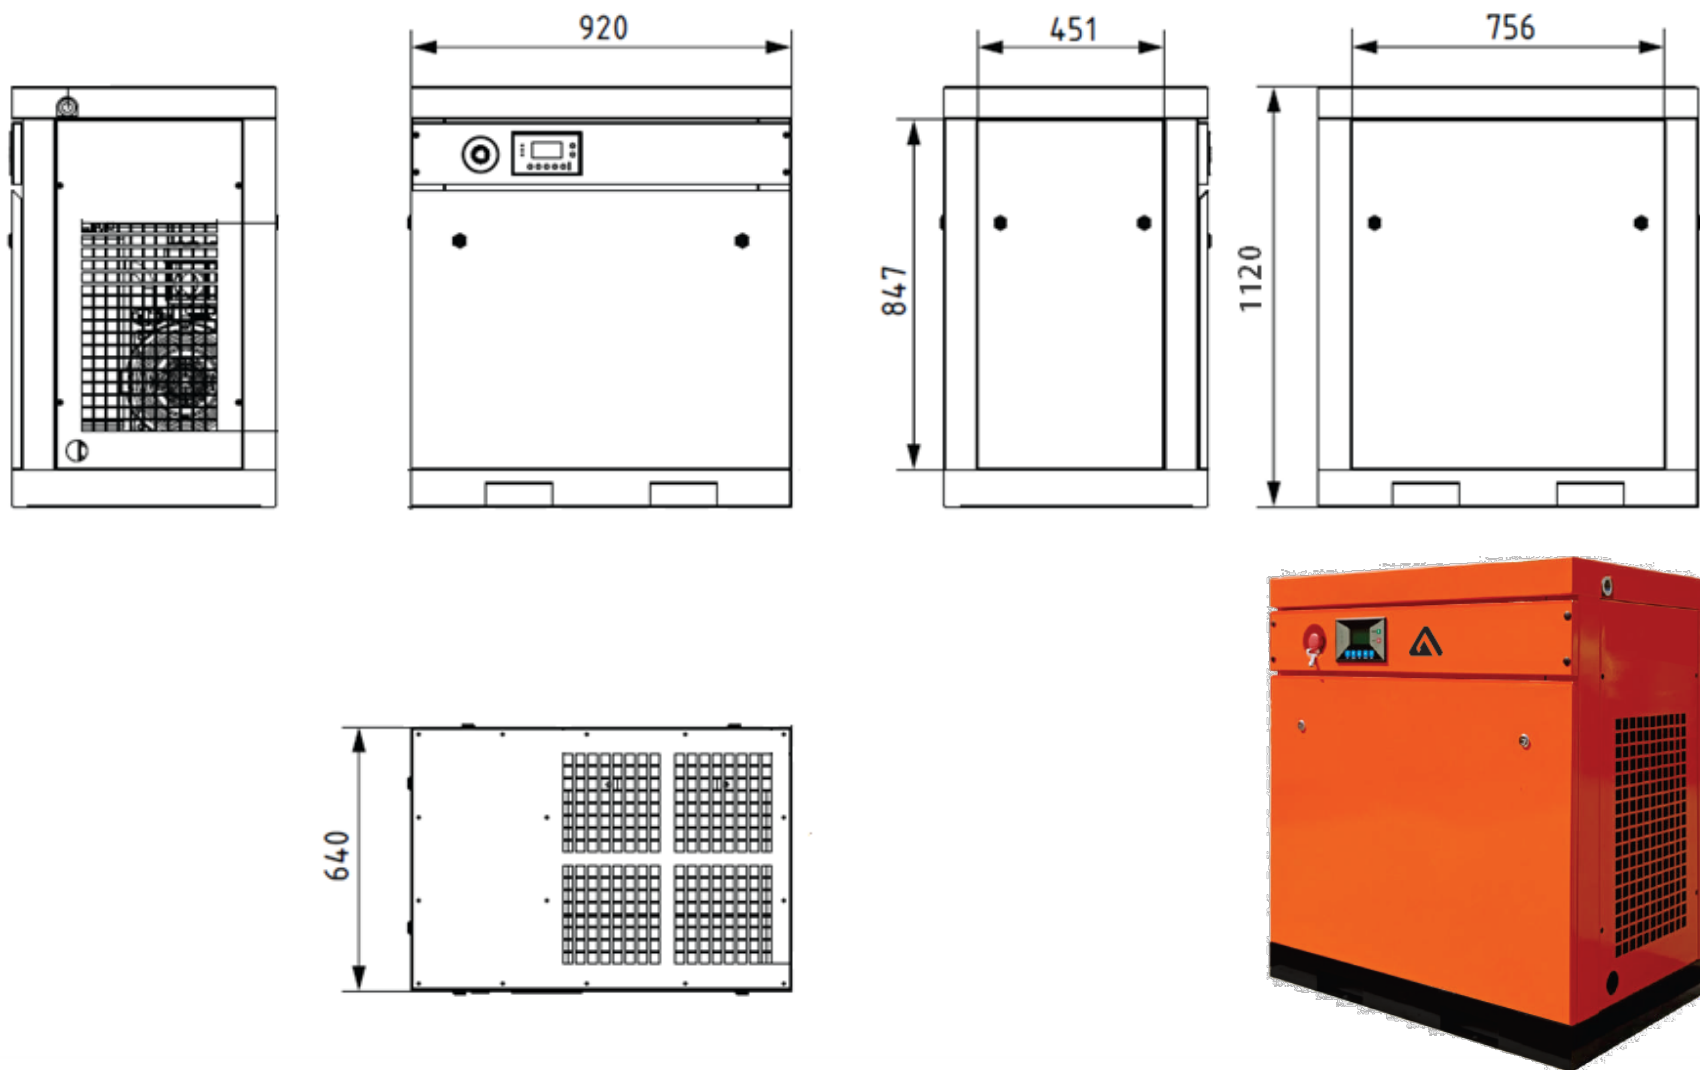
Общий вид, габаритные размеры станции компрессорной ЗИФ-СВЭ типа АРМ с двигателем 15 кВт
